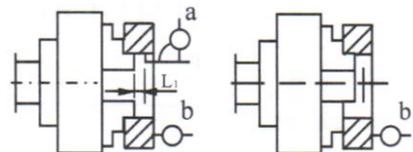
Токарный патрон с креплением заготовки за внутреннюю поверхность с помощью прямых кулачков:
